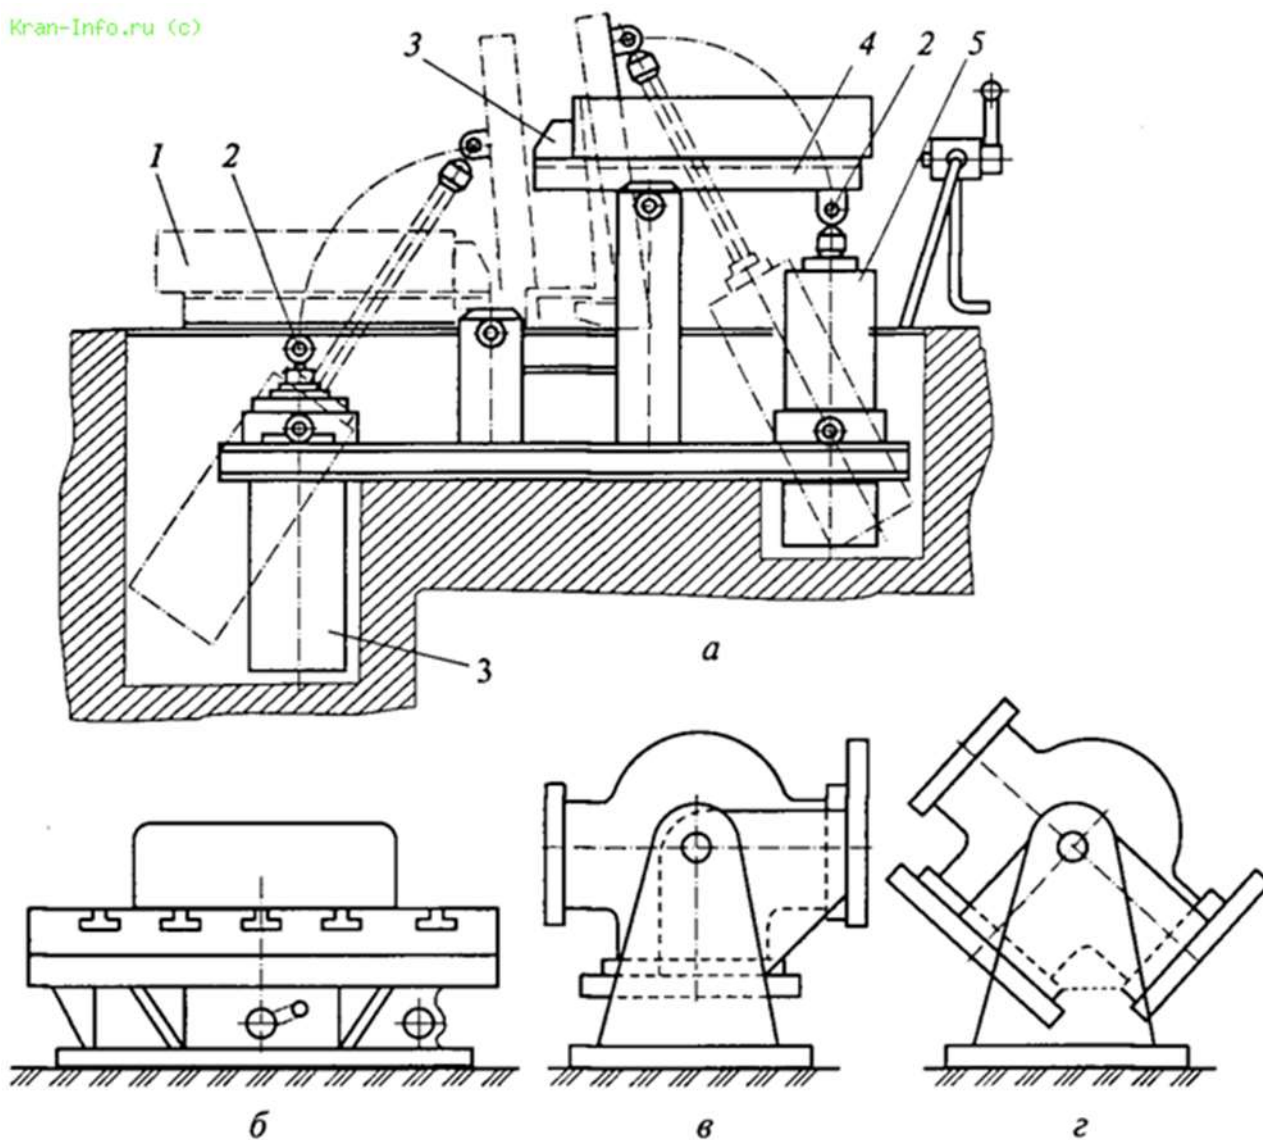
2. Кантователи пневматический (а), подвесной с электродвигателем (б) и приспособления (в, г) для кантования деталей на 90° : 1,4 — столы; 2 — ось; 3 — упор; 5 — пневматический цилиндр
